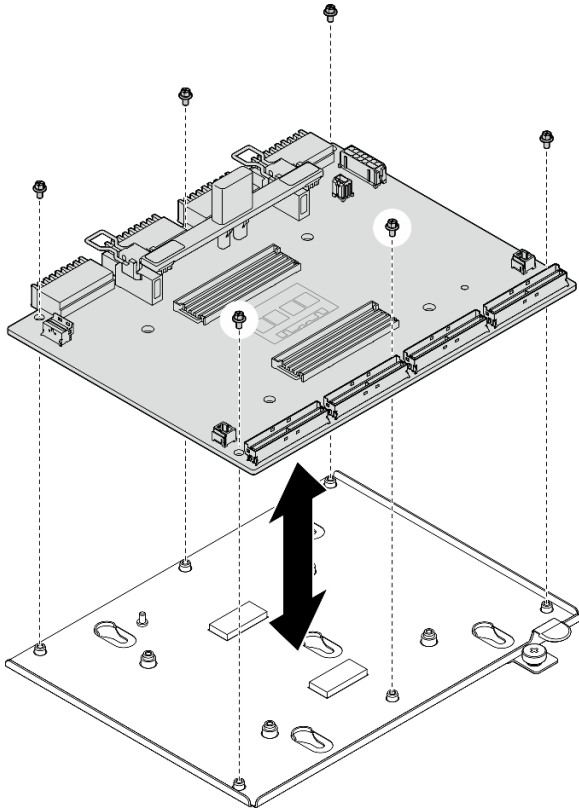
Desensamblaje de la Placa de transportador de CX-7
